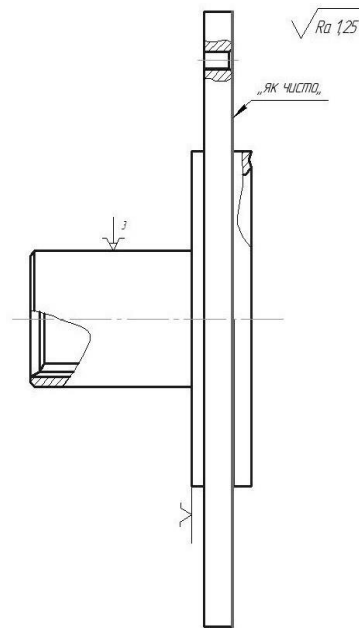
Фланець ведучої частини маточини колеса
